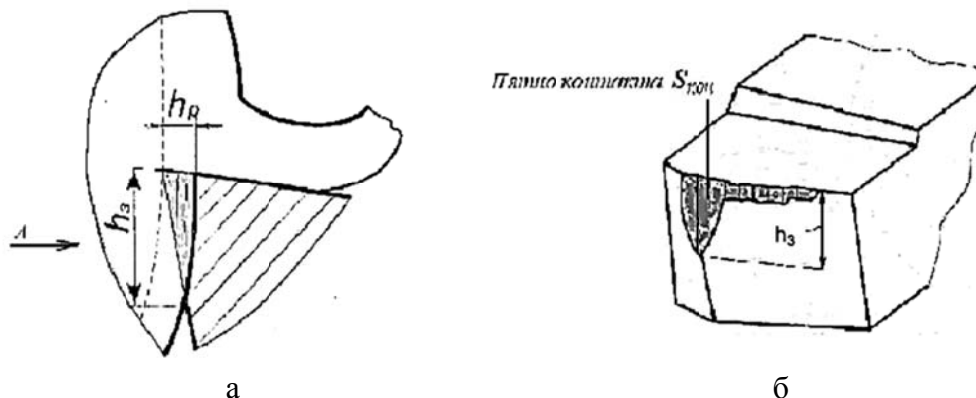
Схема взаимодействия обрабатываемой заготовки с лезвием инструмента и его износ:
